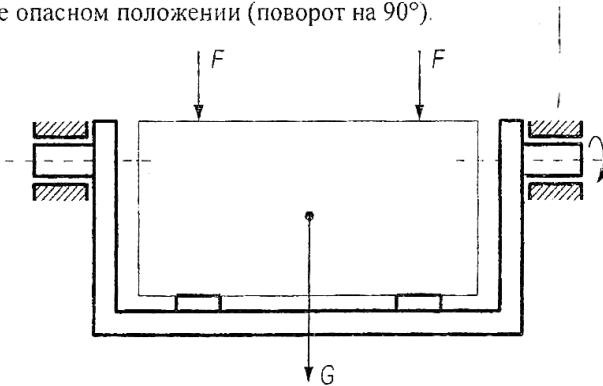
Схема установки изделия в двухстоечном приспособлении
